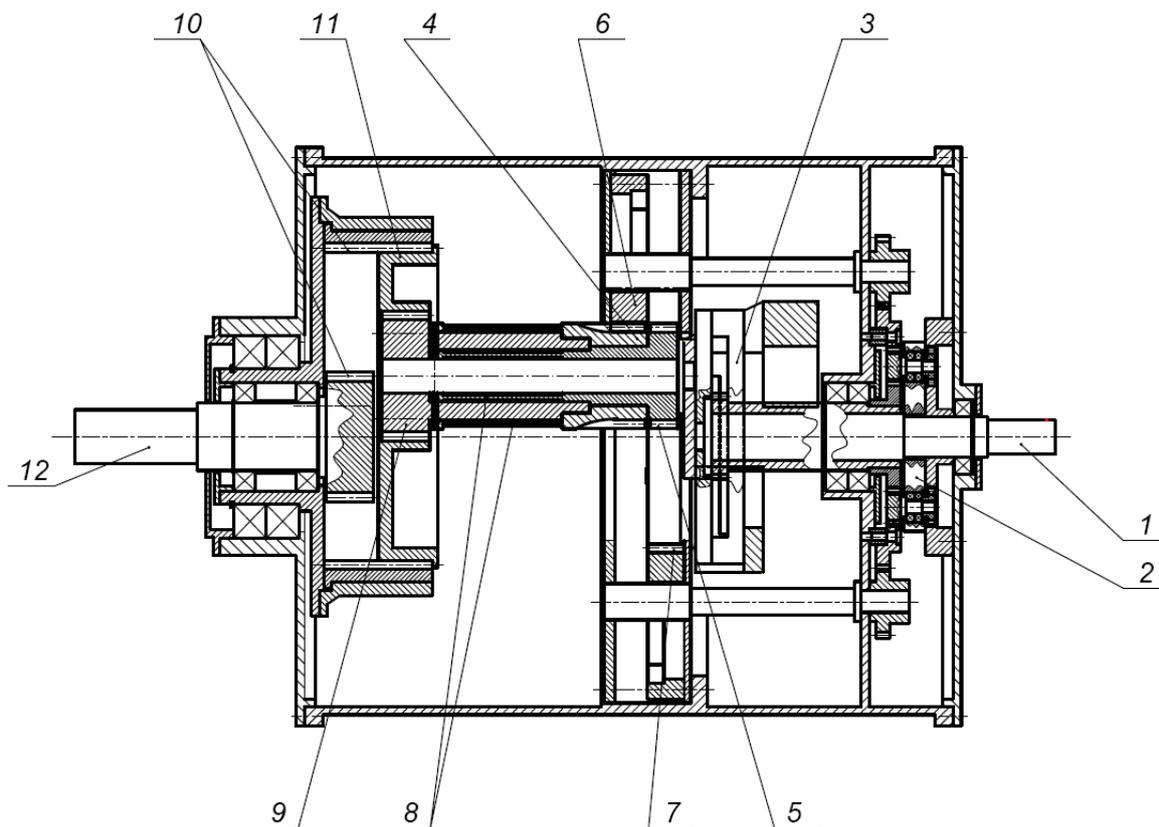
Компонновка планетарной плавнорегулируемой передачи по схеме 1: 1 – ведущий вал, 2 – механизм регулирования передаточного отношения; 3 – механизм балансировки сателлита; 4 – зубчатый венец сателлита первого силового потока; 5 – зубчатый венец сателлита второго силового потока; 6 – сектор центрального зубчатого колеса первого силового потока; 7 – сектор центрального зубчатого колеса второго силового потока; 8 – трубчатые торсионы; 9 – дополнительный зубчатый венец сателлита; 10 – планетарная передача съема вращения с сателлита; 11 – опорная вставка; 12 – выходной вал
